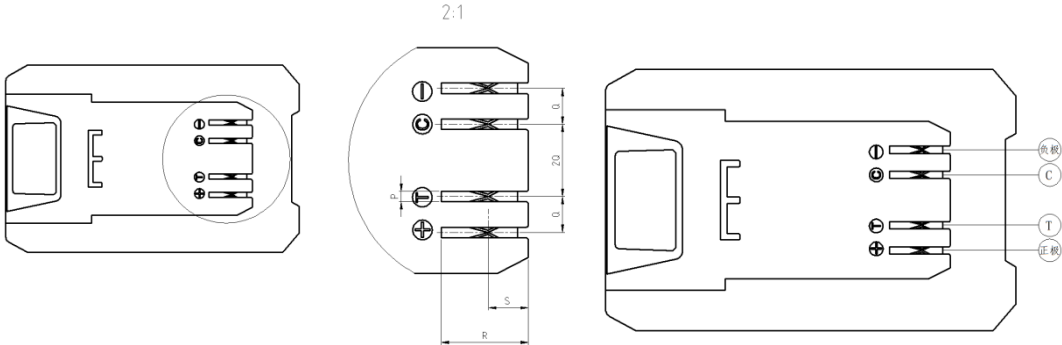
接口滑槽尺寸图 5 接口母插槽尺寸
